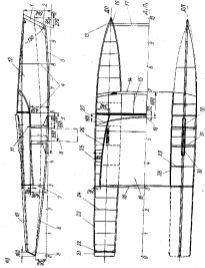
Конструктивные чертежи катера «Лилейный лист»: а — бортовой чертеж; б — план; в — вид спереди.
